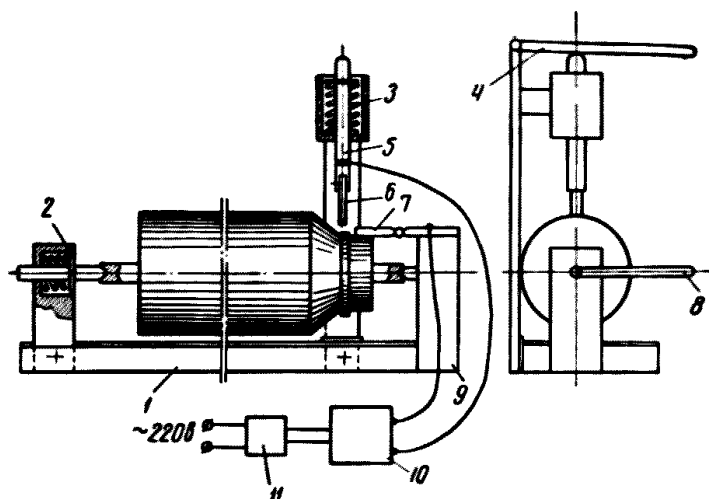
Установка для паяния коллекторов твердыми припоями.
